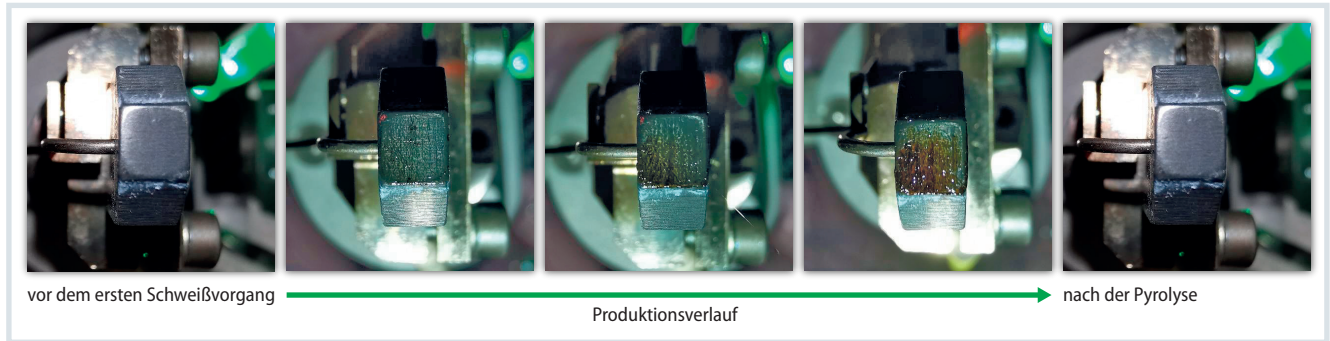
Die Schmutzschicht nimmt mit der Anzahl der Schweißungen zu, bis sich die Schweißqualität verschlechtert. Die turnusmäßige Pyrolyse stellt eine dauerhaft hohe Schweißqualität sicher. © Engel
